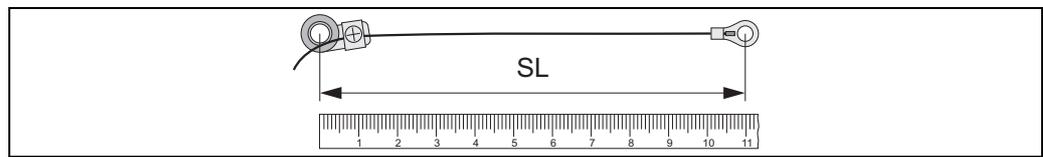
Fixierteil (a) und Kabelschuhe (b) mit einem Abstand entsprechend der Schnurlänge (SL)
